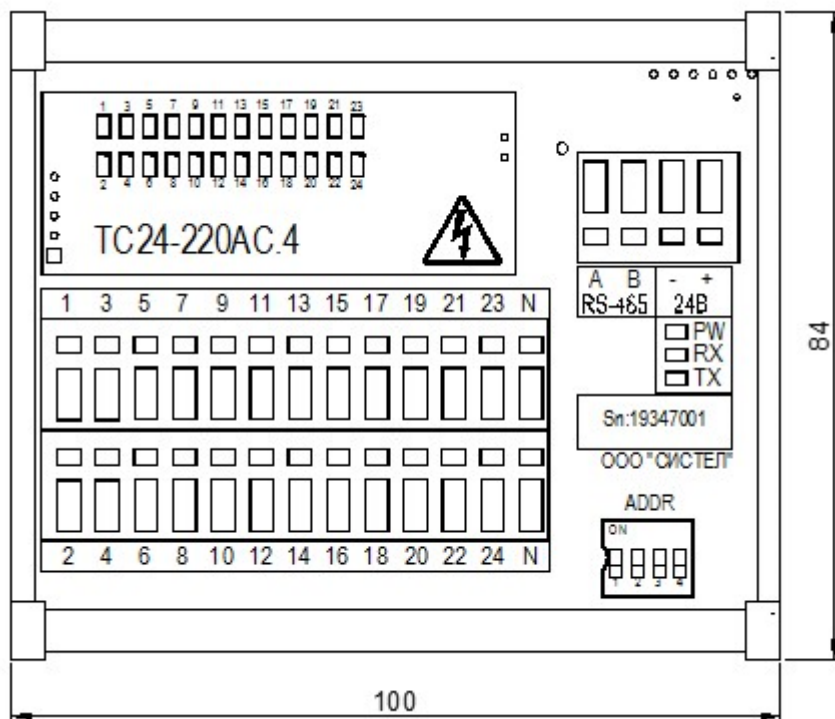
Внешний вид и габаритные размеры Устройства
